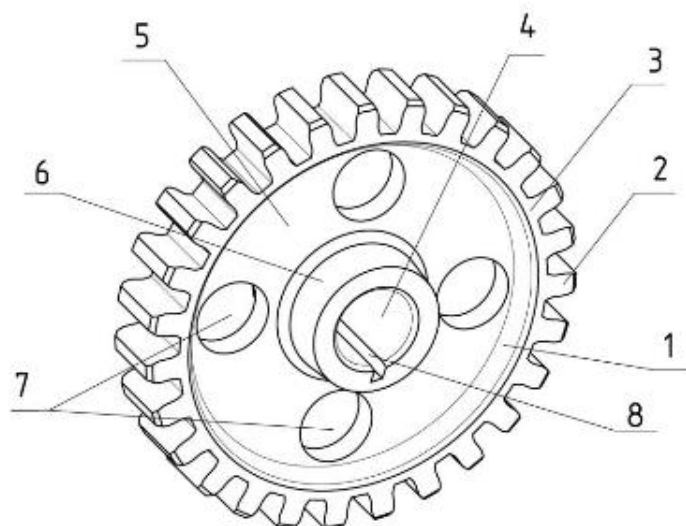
Строение зубчатого цилиндрического штампованного колеса: 1 – обод; 2 – зуб; 3 – венец; 4 – посадочное отверстие; 5 – диск; 6 – ступица; 7 – отверстие в диске; 8 – шпоночный паз
